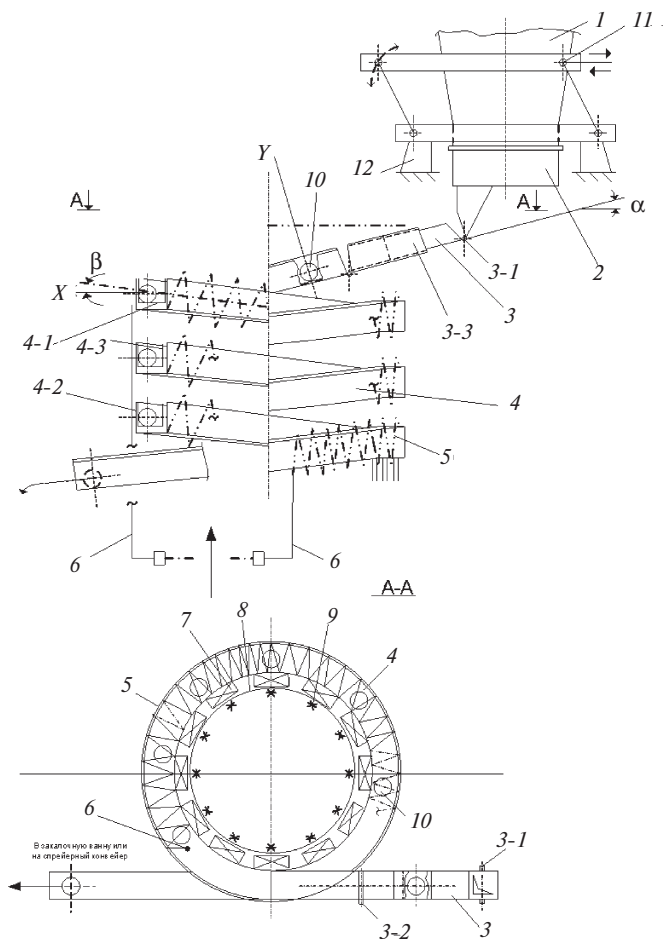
Установка непрерывного действия для индукционного нагрева изделий шарообразной формы
